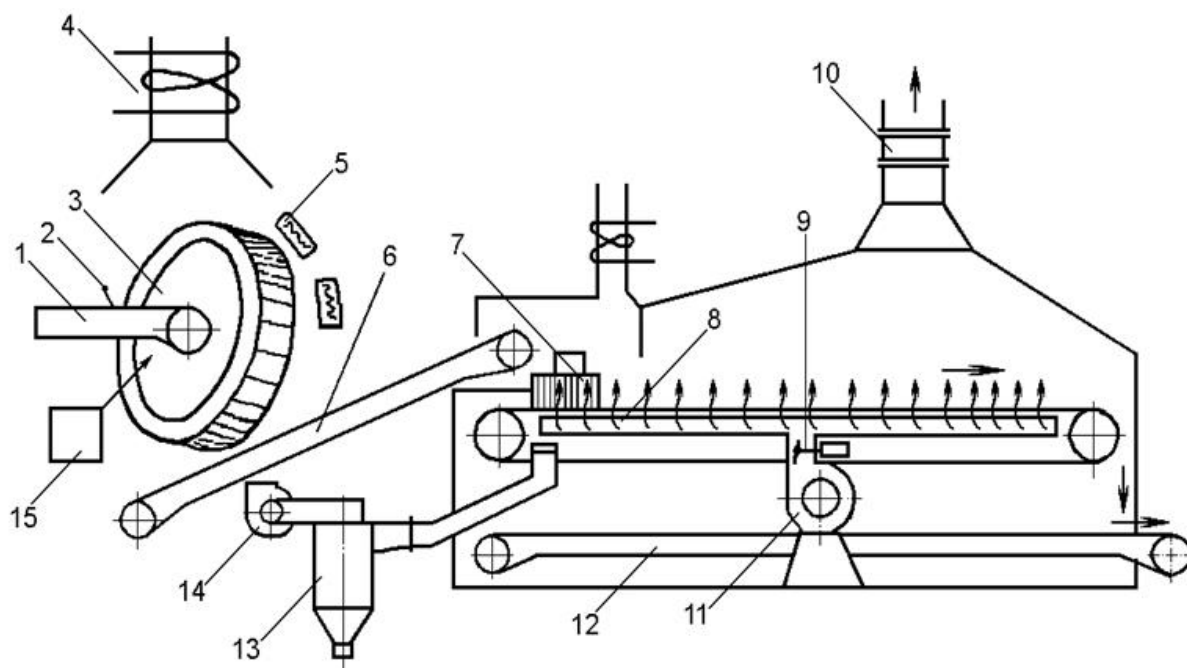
Схема установки Фишера для охлаждения отработанной формовочной смеси с гомогенизатором:
